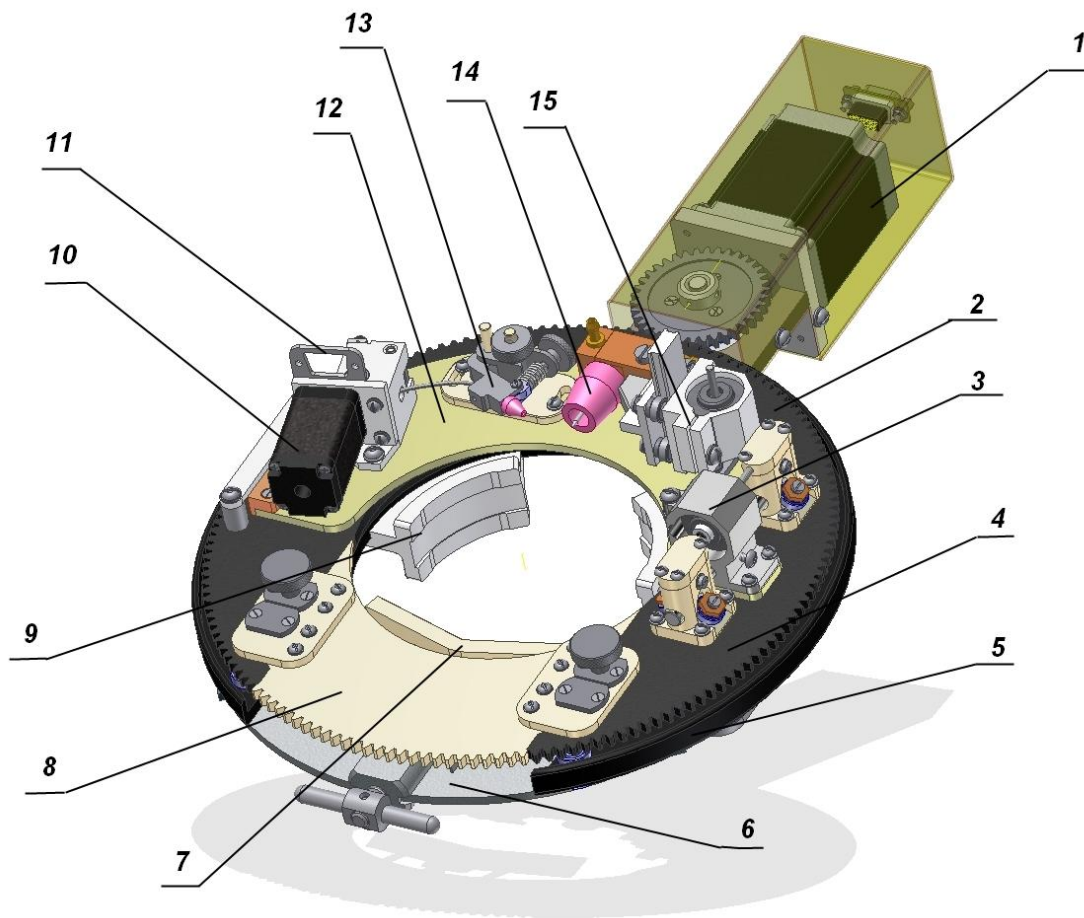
Конструкция сварочной головки ГНС 140
